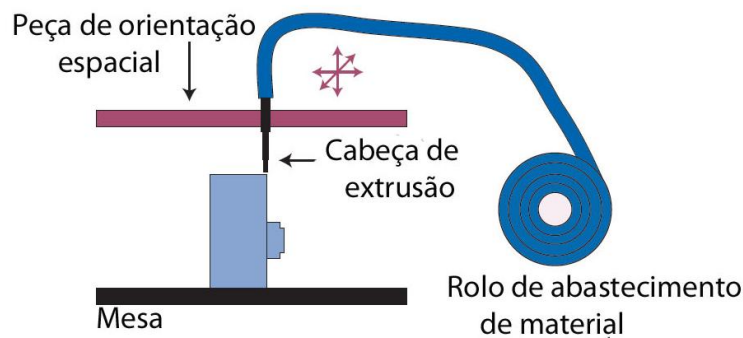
Dispositivo de impressão de modelagem por deposição de material fundido. Adaptado de [86]
